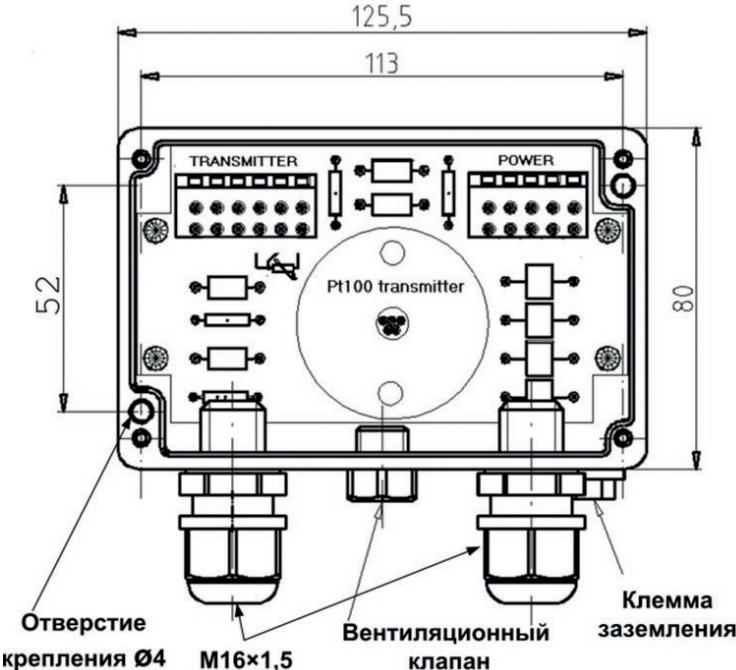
Внешний вид корпуса со снятой крышкой
